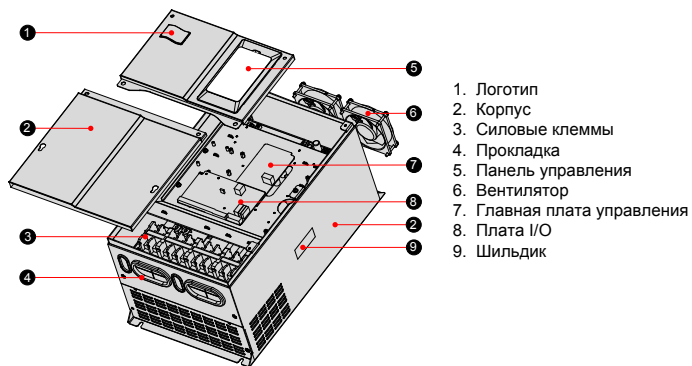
Общий вид ME320LN (18.5–45 кВт, металлический корпус)
